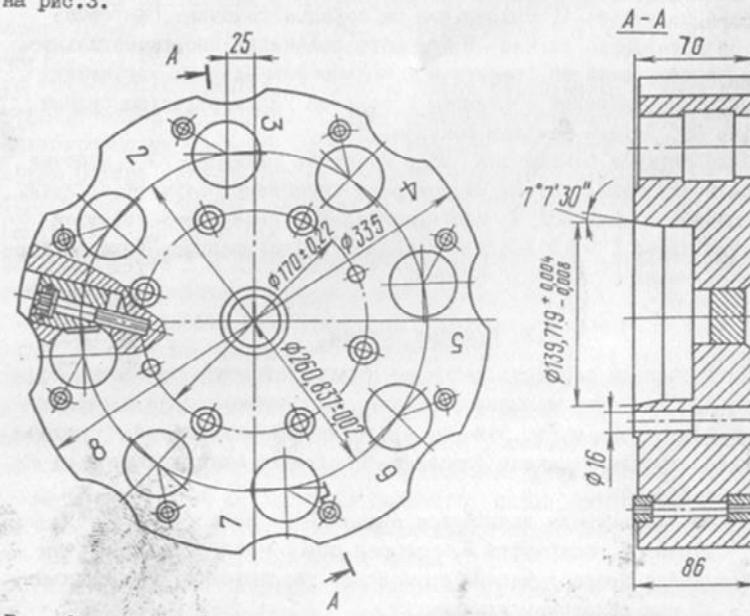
Инструментальный диск восемьпозиционный УГ9326.0300.000
